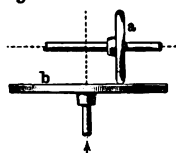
Planrad und Rad mit balliger Umfangsfläche.
